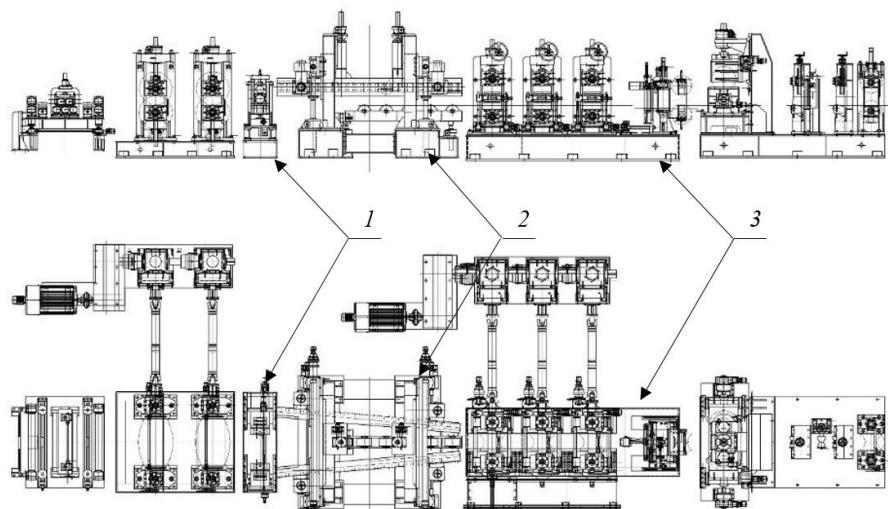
Схема формовочного стана ТЭСА 355 «ADDA FER MECCANICA»:
